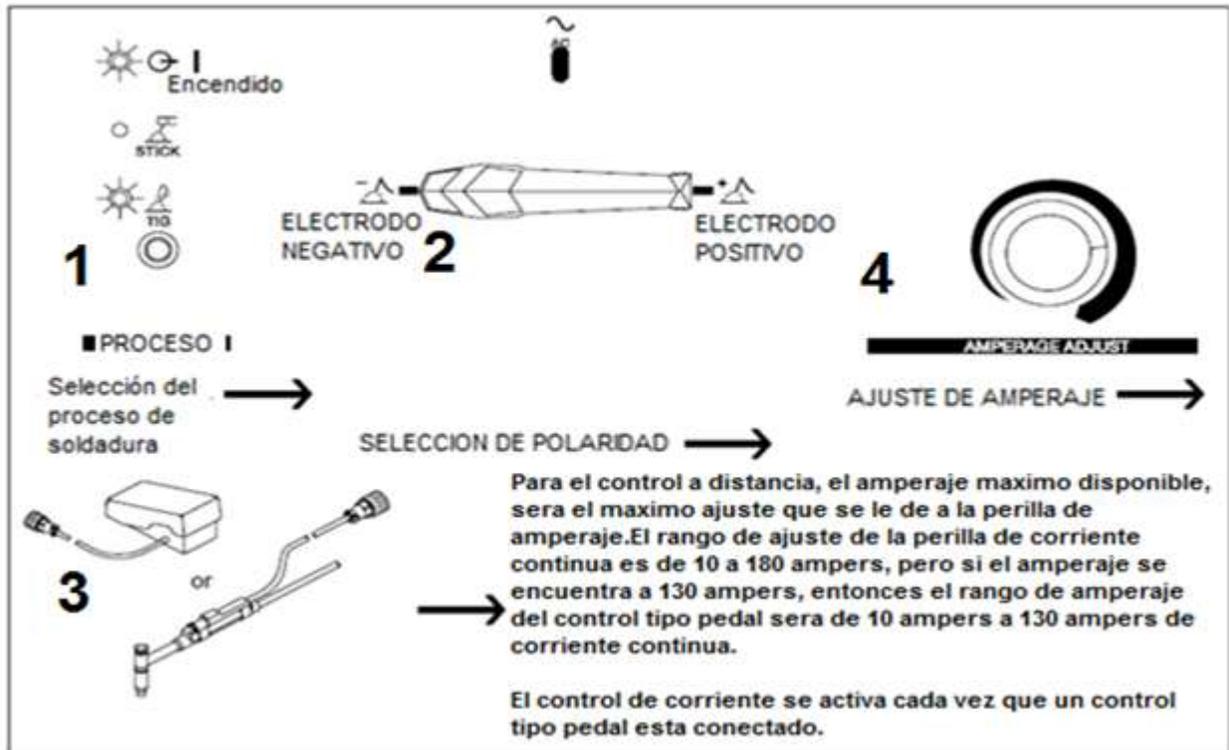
Muestra los pasos a realizar para un ajuste con soldadura TIG
